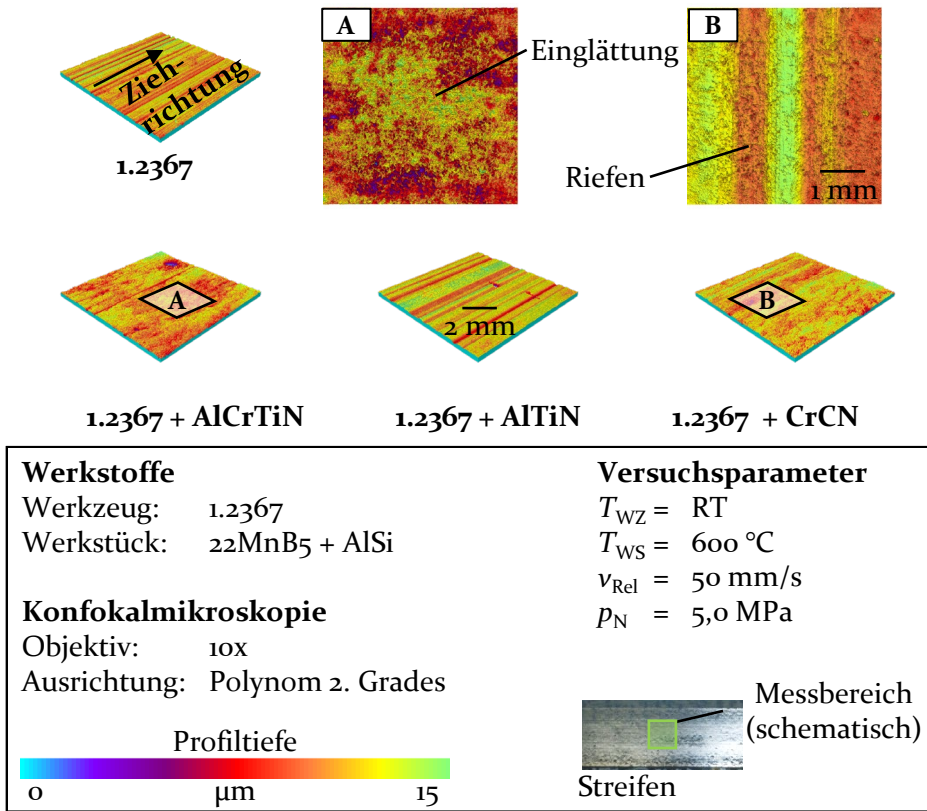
Topographieaufnahmen der Werkstückoberfläche für unterschiedliche Werkzeugbeschichtungen
